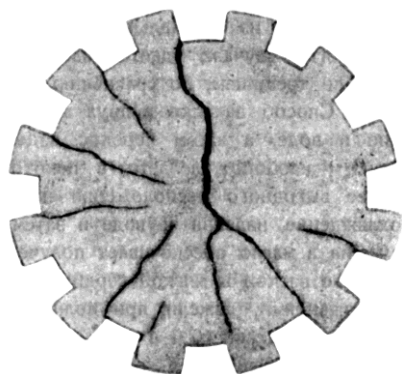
Поперечный разрез валика зацепления с продольными фрезерованными канавками (макрошлиф нетравлен)
